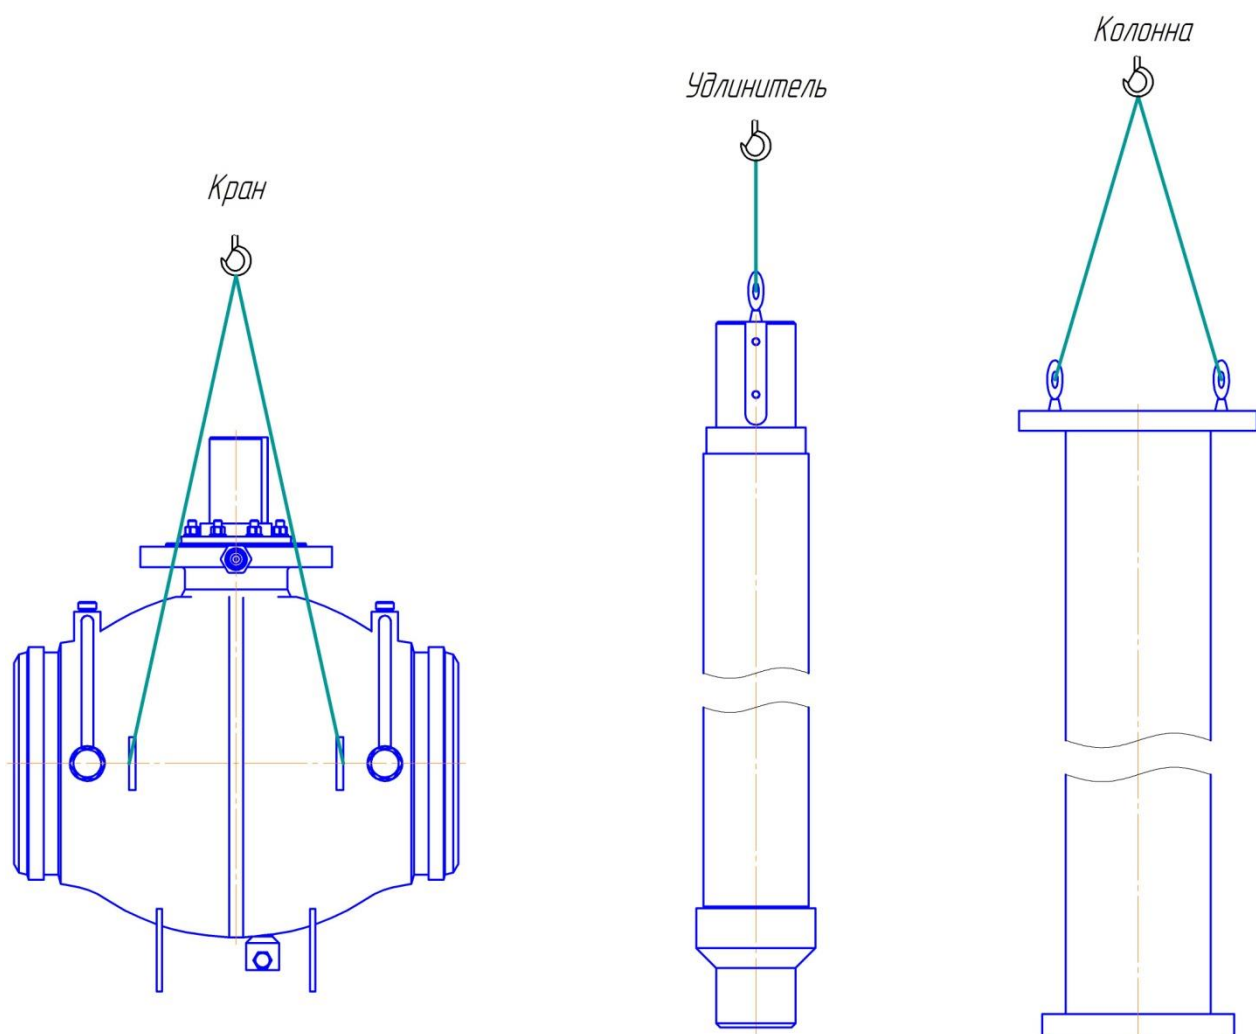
Схема строповки при монтаже узлов подземного крана (рекомендуемая)
